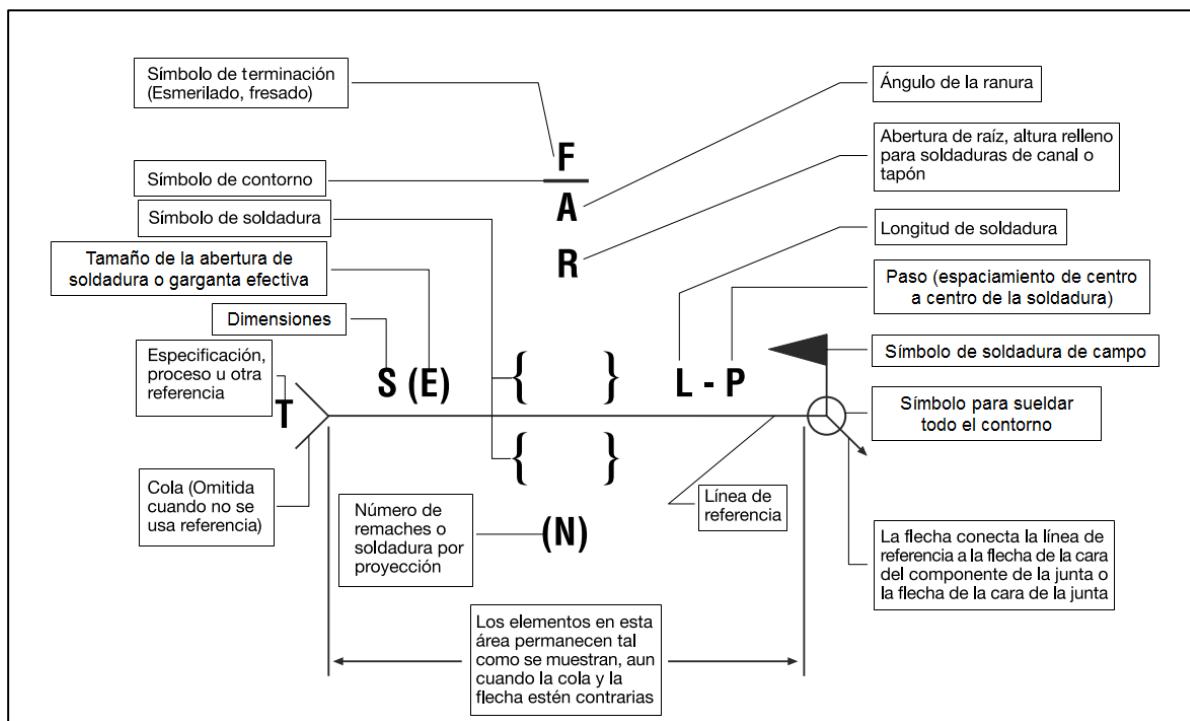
Ubicación De Cada Elemento En El Símbolo De Soldadura [7, 85 y 86].
